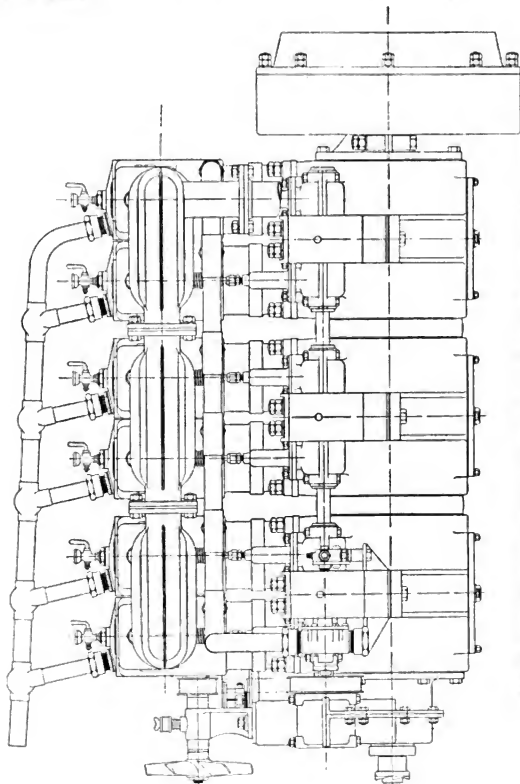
Sechszylindermotor des »Hexe«-Wagens, gebaut von der Firma Achenbach & Co., Hamburg I.
